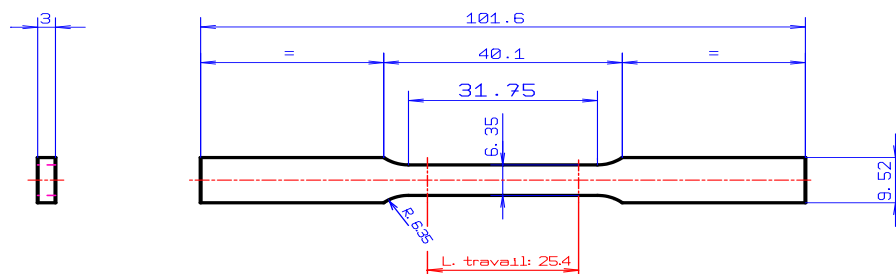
Dessin de l'éprouvette de traction [31] - côtes en mm.
